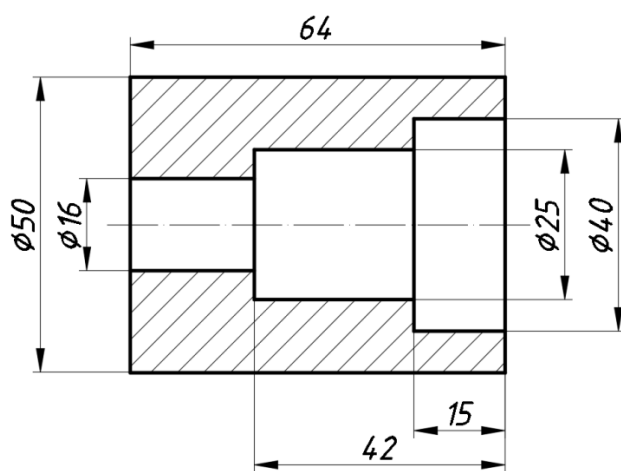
Образец выполнения чертежа с внутренними ступенчатыми отверстиями.
